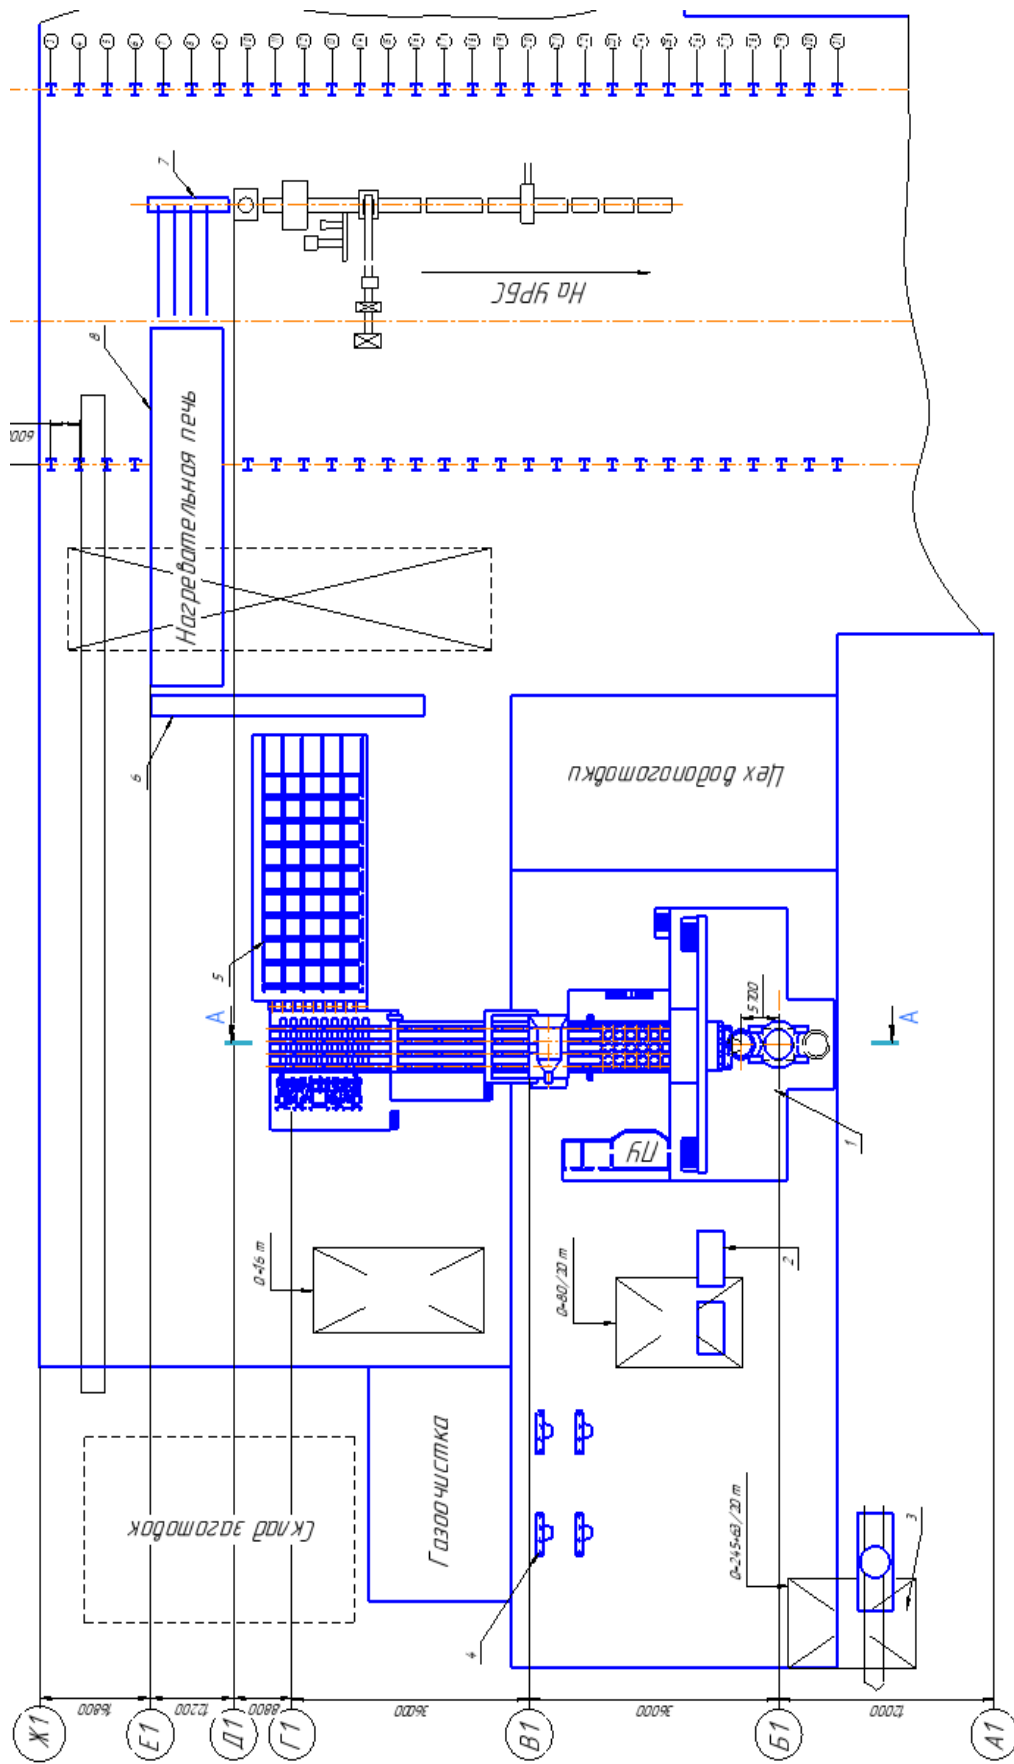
Участок непрерывной разливки фасонной заготовки
